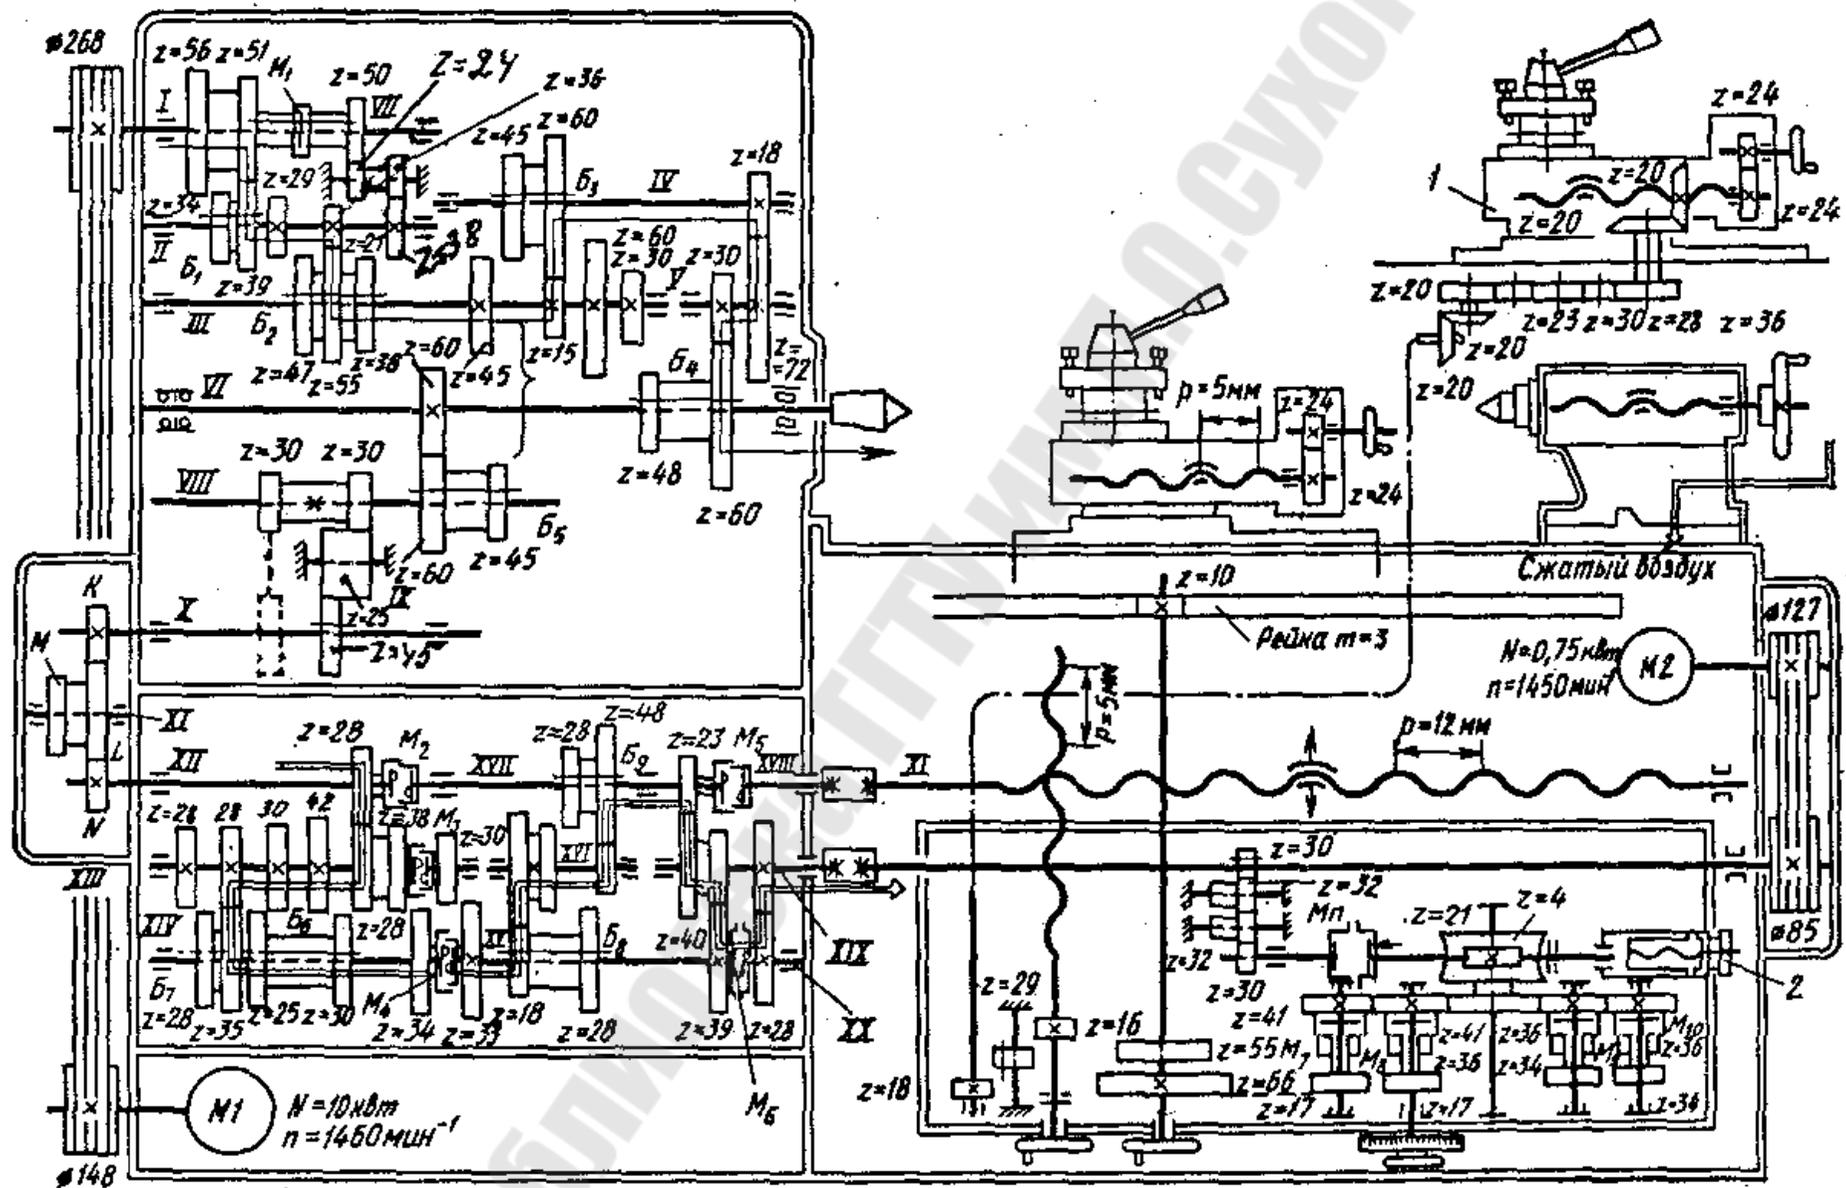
Кинематическая схема токарно-винторезного станка
